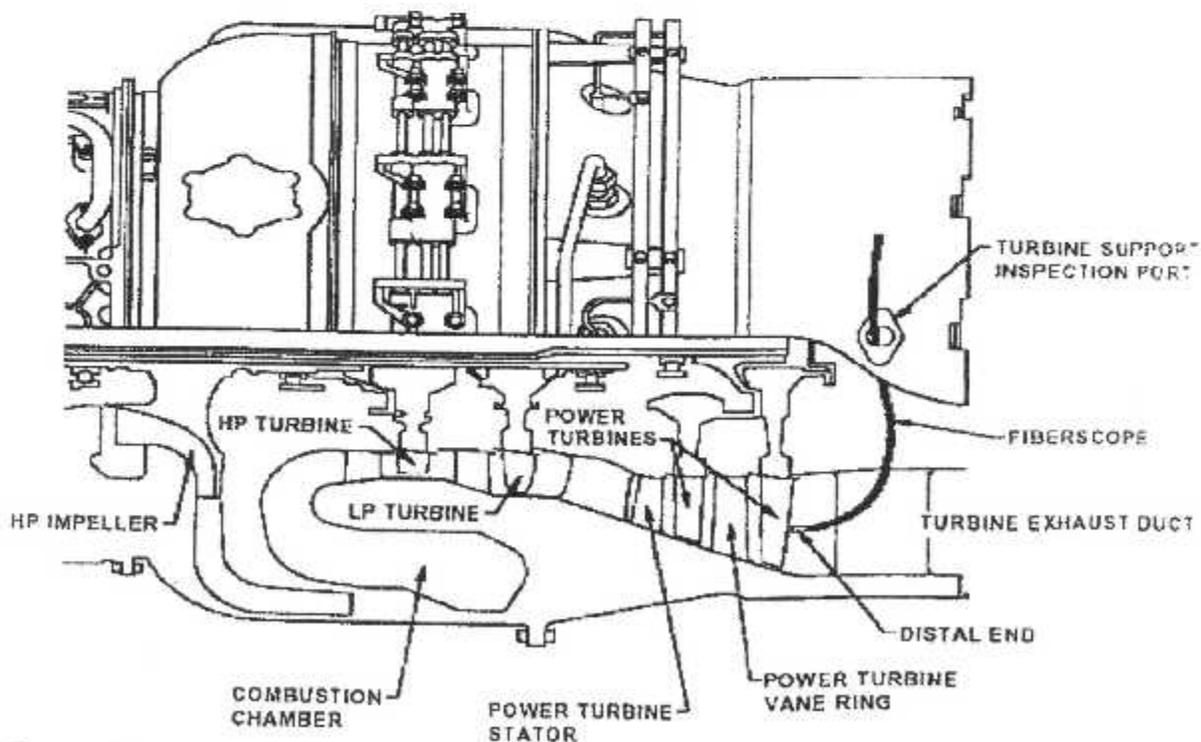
Inspection boroscopique des ailettes du 2^{ème} étage de la tub lib.
